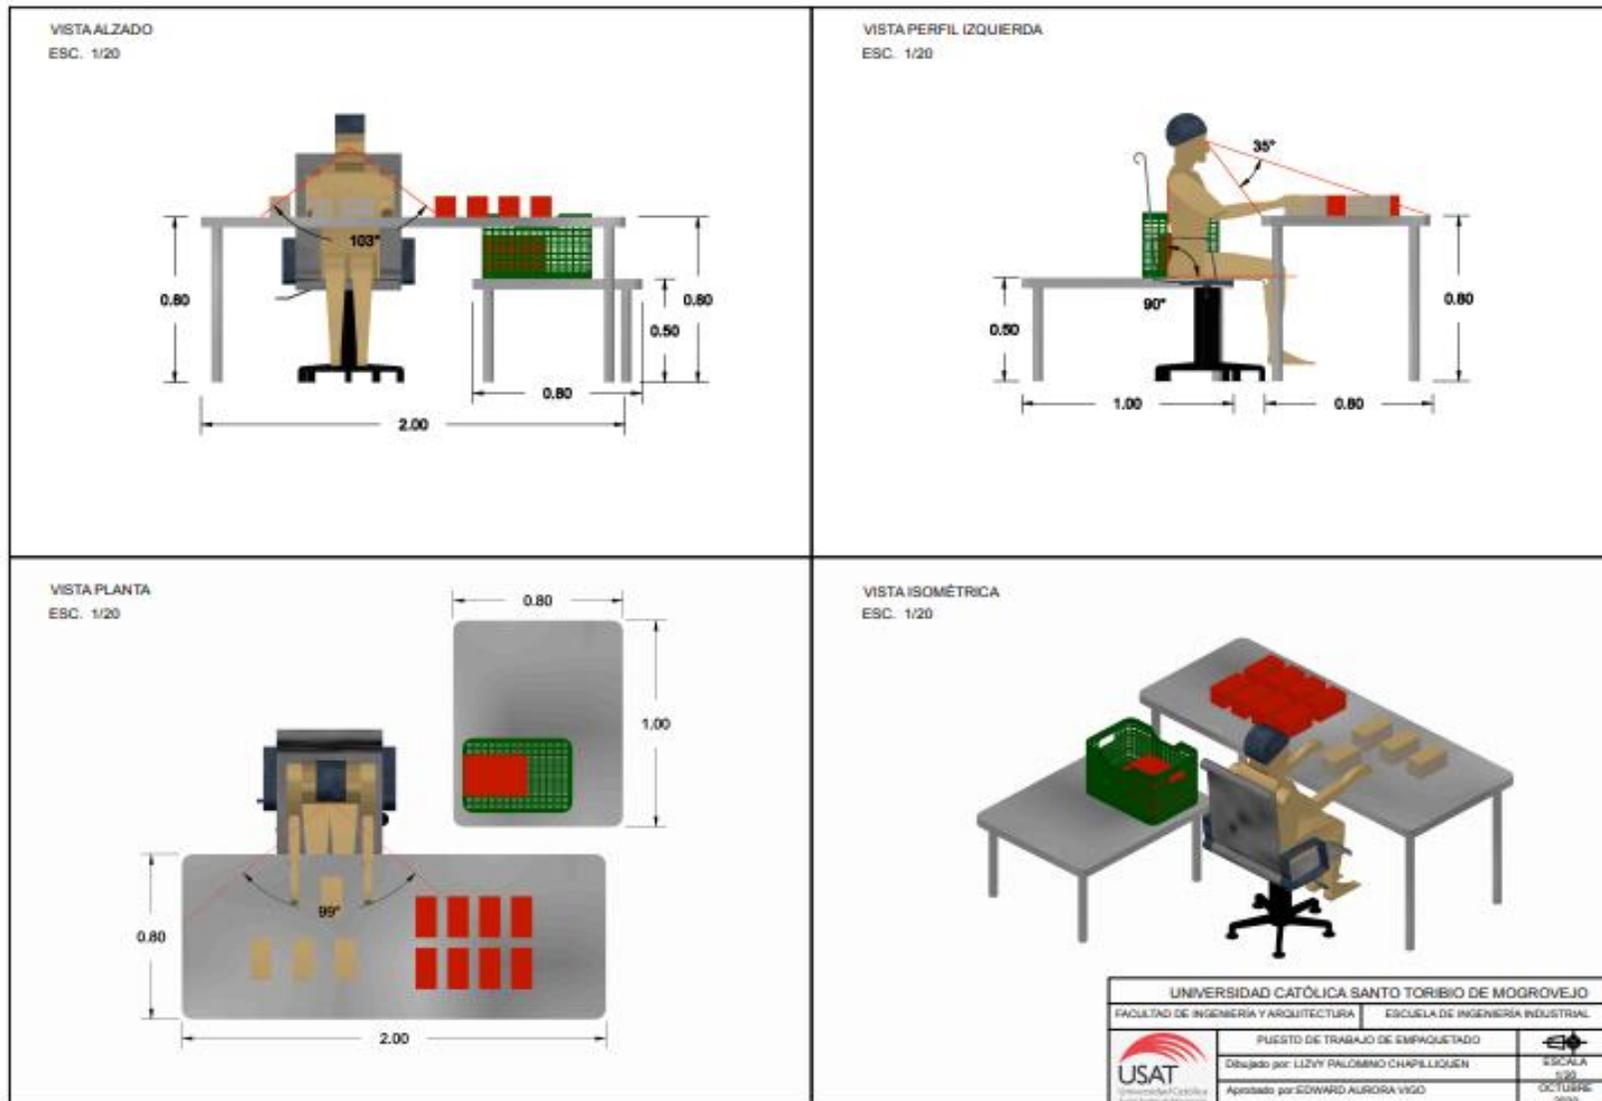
Vistas del puesto de trabajo mejorado de empaquetado.
